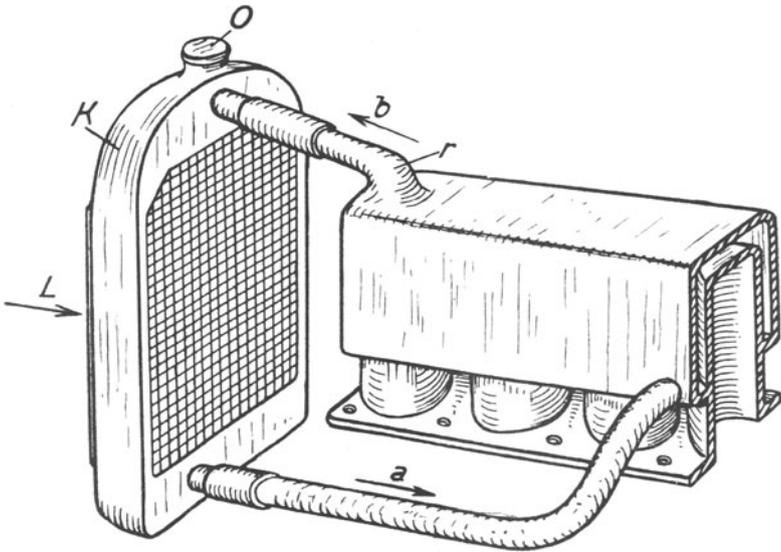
Vierzylinder mit Wasserkühlung durch natürlichen Kreislauf des Kühlwassers (Thermosiphon) — *K* Kühler
